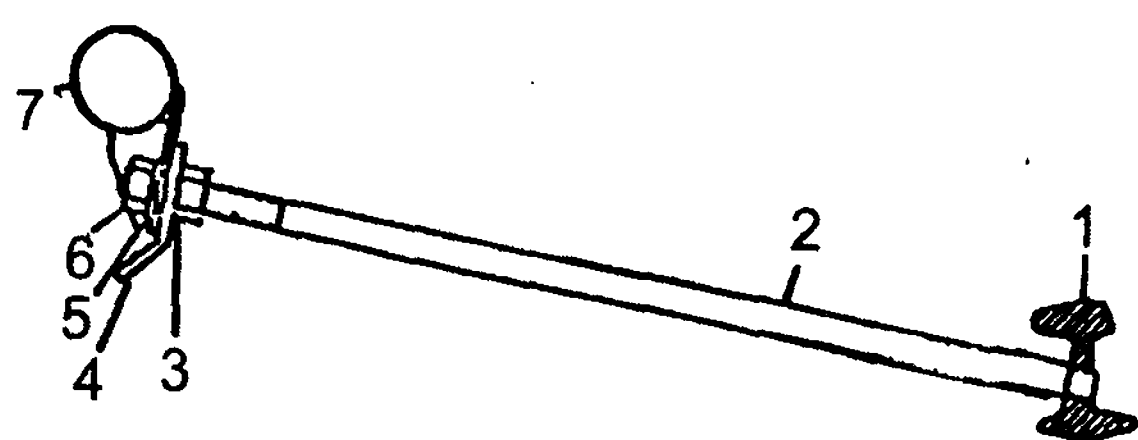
Установка растяжки передней подвески: 1 – балка-поперечина; 2 – растяжка; 3, 6 – гайки; 4 – скоба; 5 – шайба; 7 – поперечина рамы
